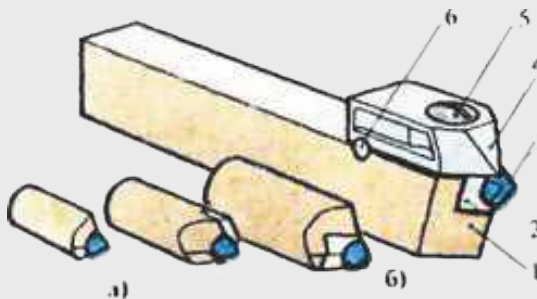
Алмазні різці: а — вставний кристал алмазу; б — механічне кріплення алмазного кристала; 1 — державка; 2 — підкладка; 3 — алмаз; 4 — прижимна планка; 5 — гвинт; 6 — опора
